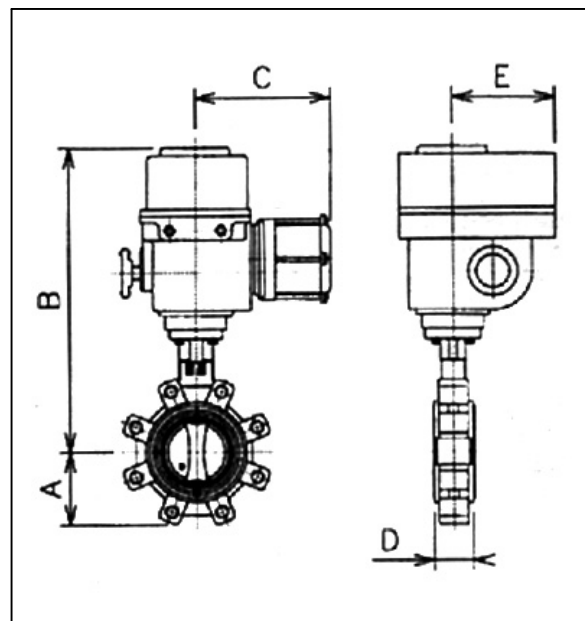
Габаритные и присоединительные размеры SYLAX – ELEC 380 с фланцем типа - 8 отверстий.
